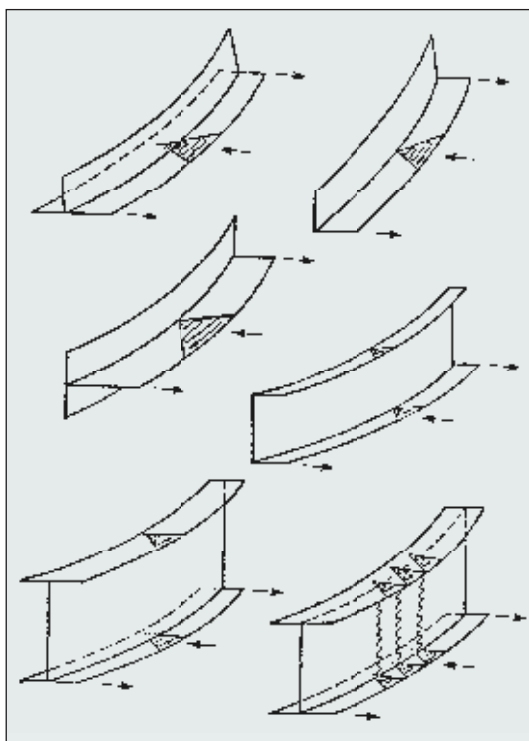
Последовательность движения горелок при нагреве прямоугольников на широких полках (стрелками показано направление движения горелки)
